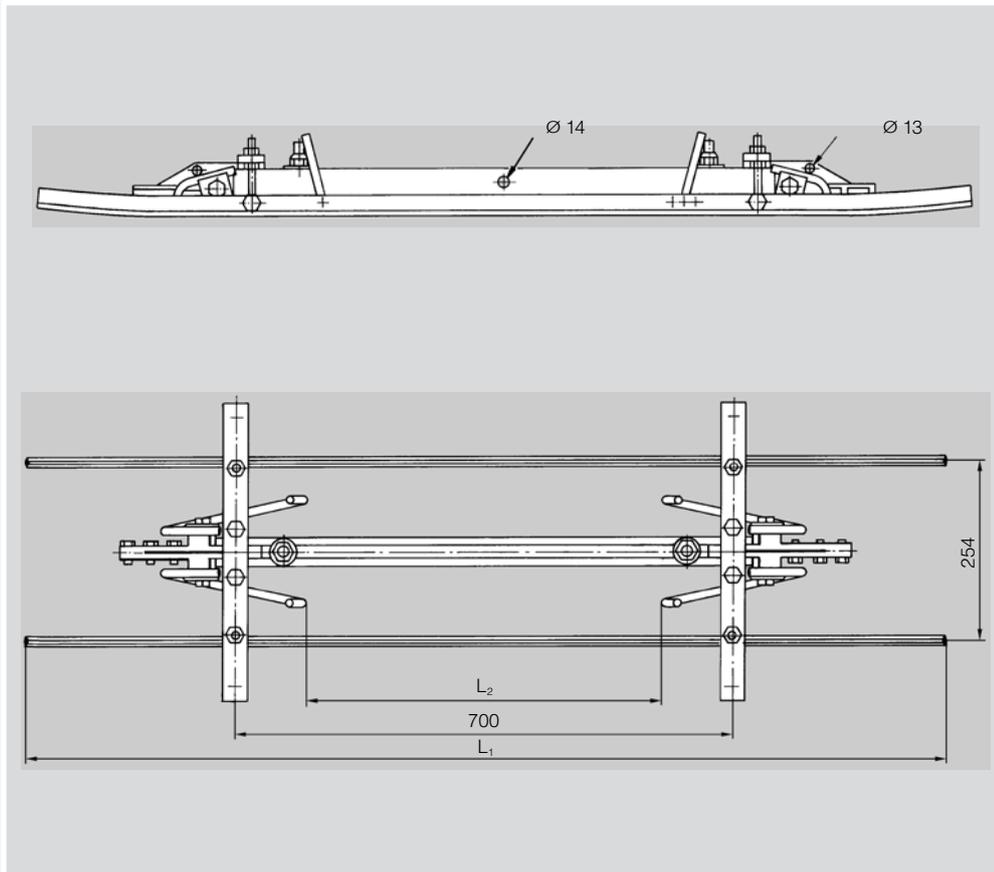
Streckentrenner mit Cu-Gleitkufen, mit einfacher und verstärkter Isolation
